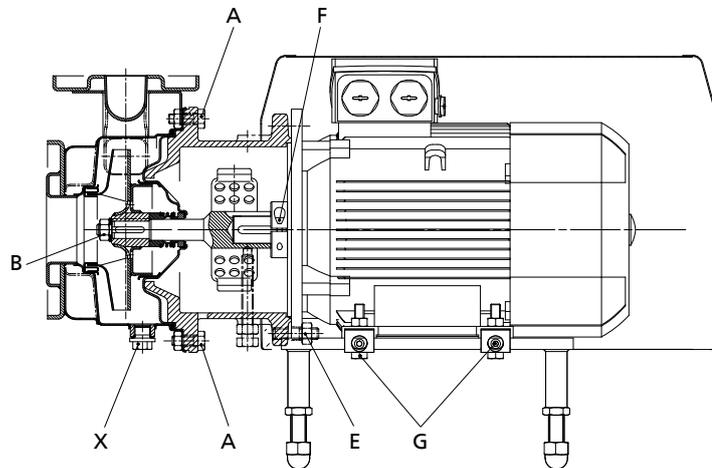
Schraubenanzugstellen für Etachrom B 050-025-125.1, 050-025-125, 050-025-160, 050-025-200, 050-032-125.1, 050-032-125, 050-032-160, 050-032-200, 065-040-125, 065-040-160, 065-040-200, 065-050-125, 065-050-160
